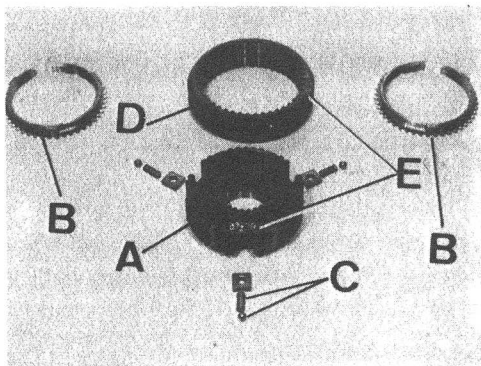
Conjunto sincronizador 3a y 4a V.
